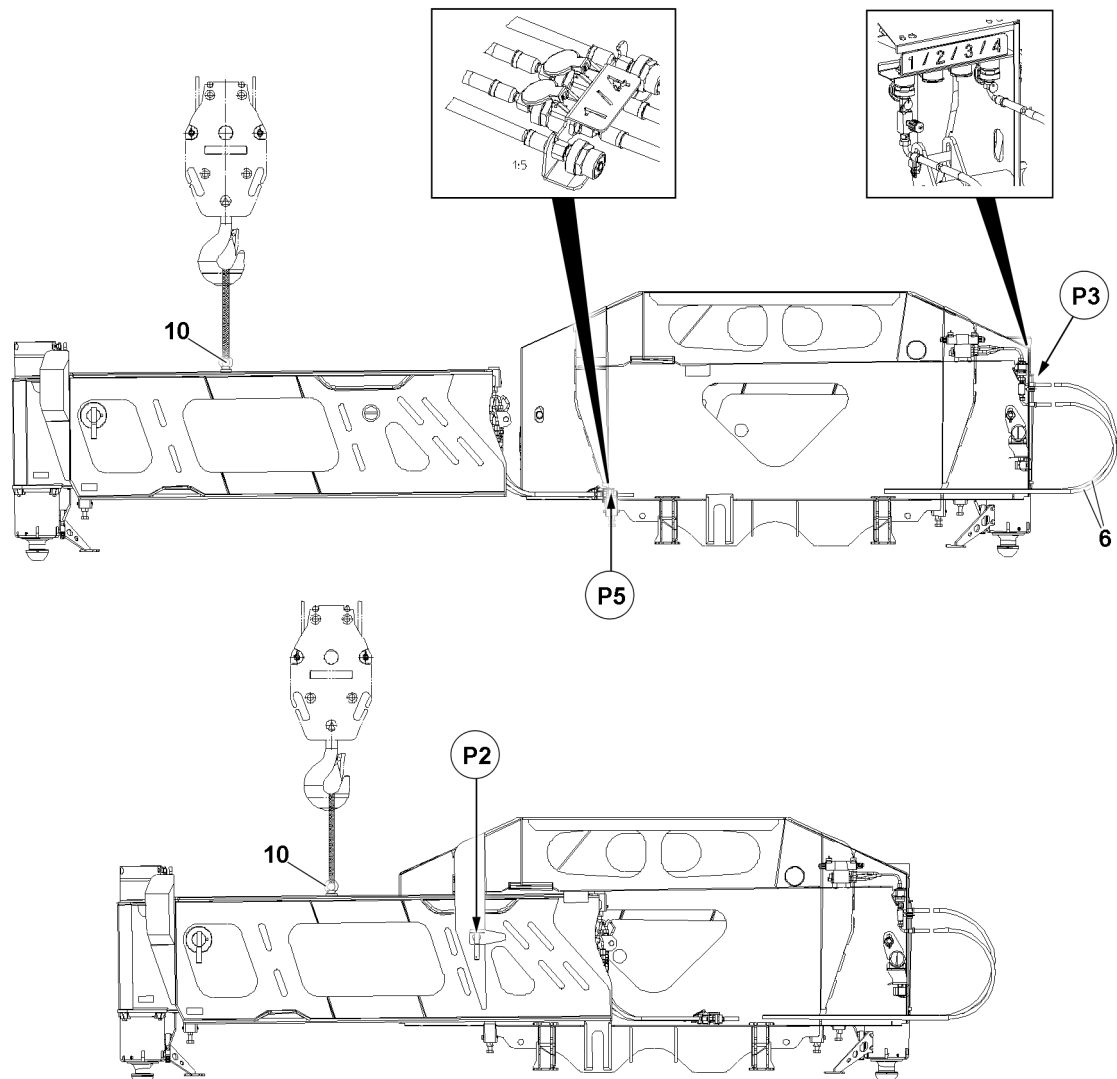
Erguer a viga móvel para a caixa da viga móvel
